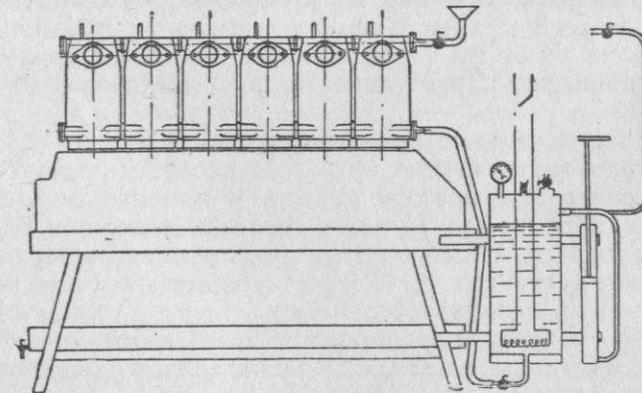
Установка для гидропневматического испытания рубашек цилиндров.
